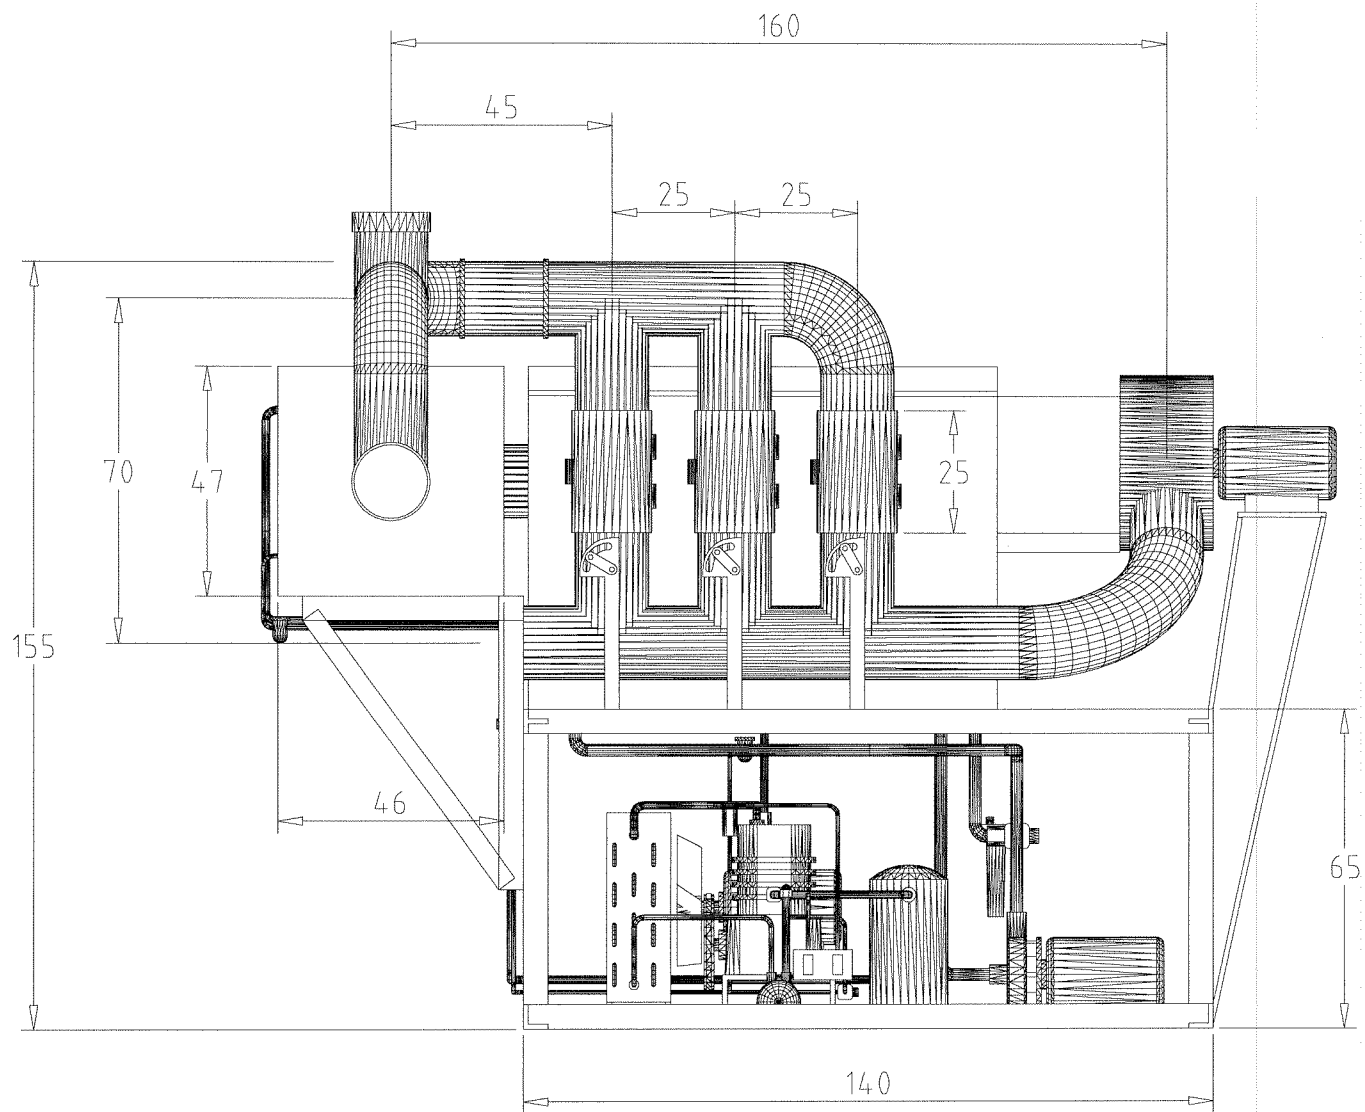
Vista frontal do SIGEP com indicação das dimensões mais relevantes, medidas em cm.
